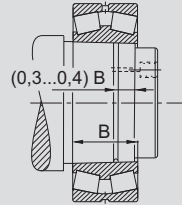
Desmontagem de Eixo Cônico com o uso de Pressão Hidráulica
